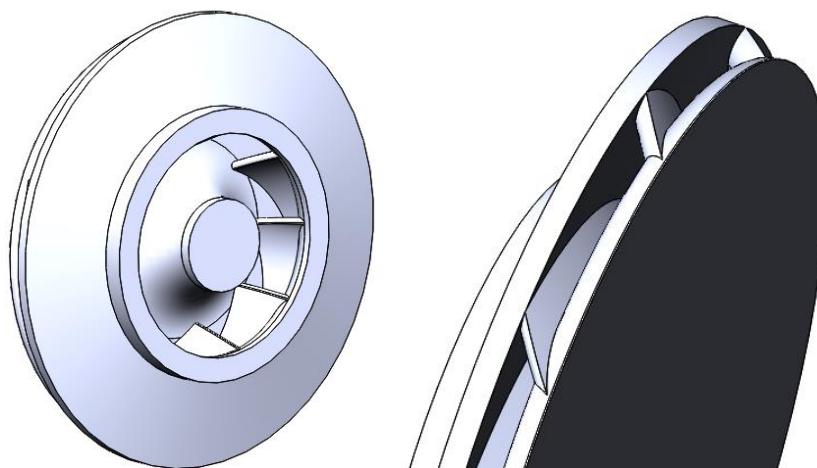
Общий вид рабочего колеса по первой схеме
